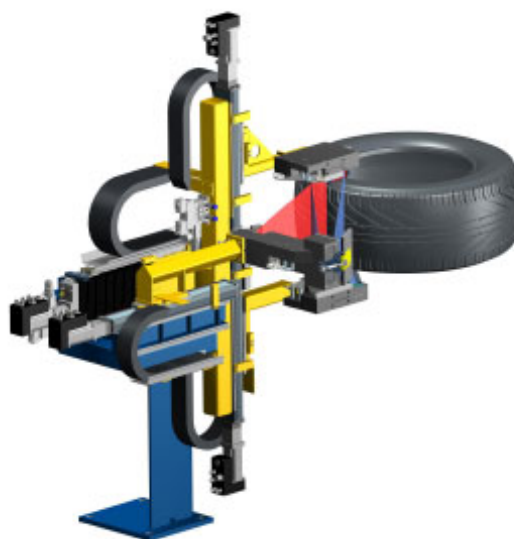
Sensor *Sheet-of-Light* Laser [13].
